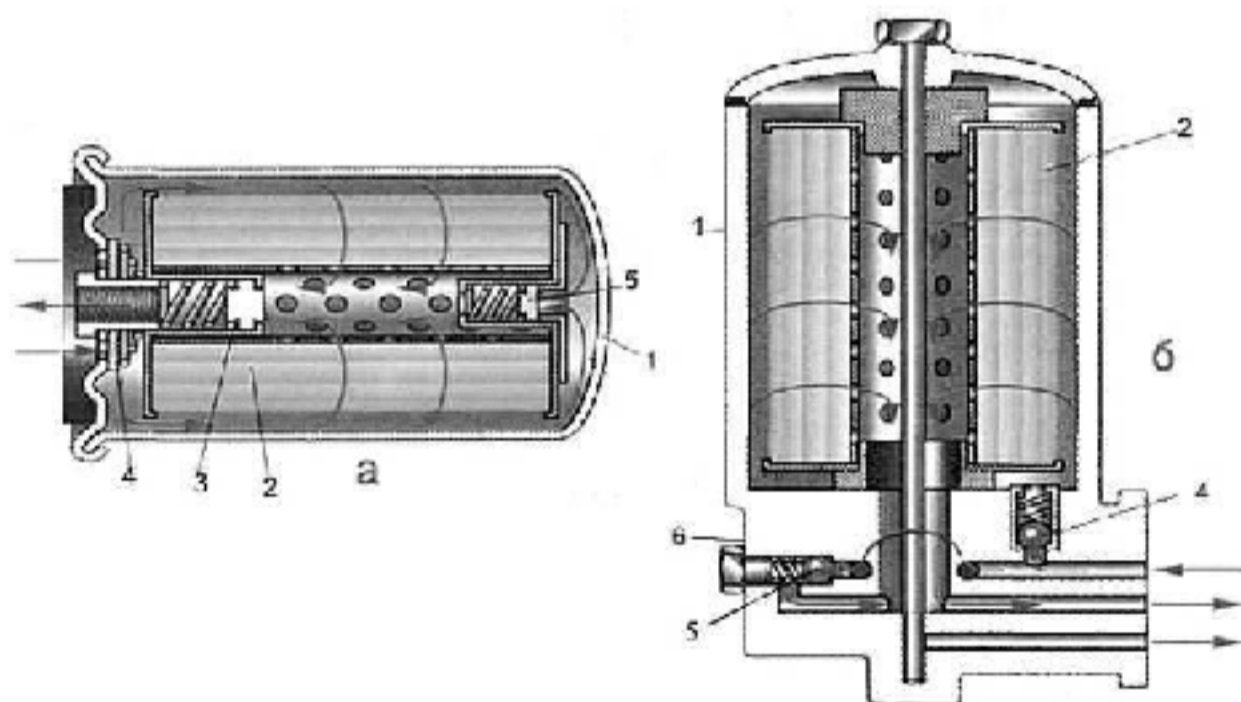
Устройство масляного фильтра: а- неразборный; б- разборный; 1- корпус,2- фильтрующий элемент,3- обратный
